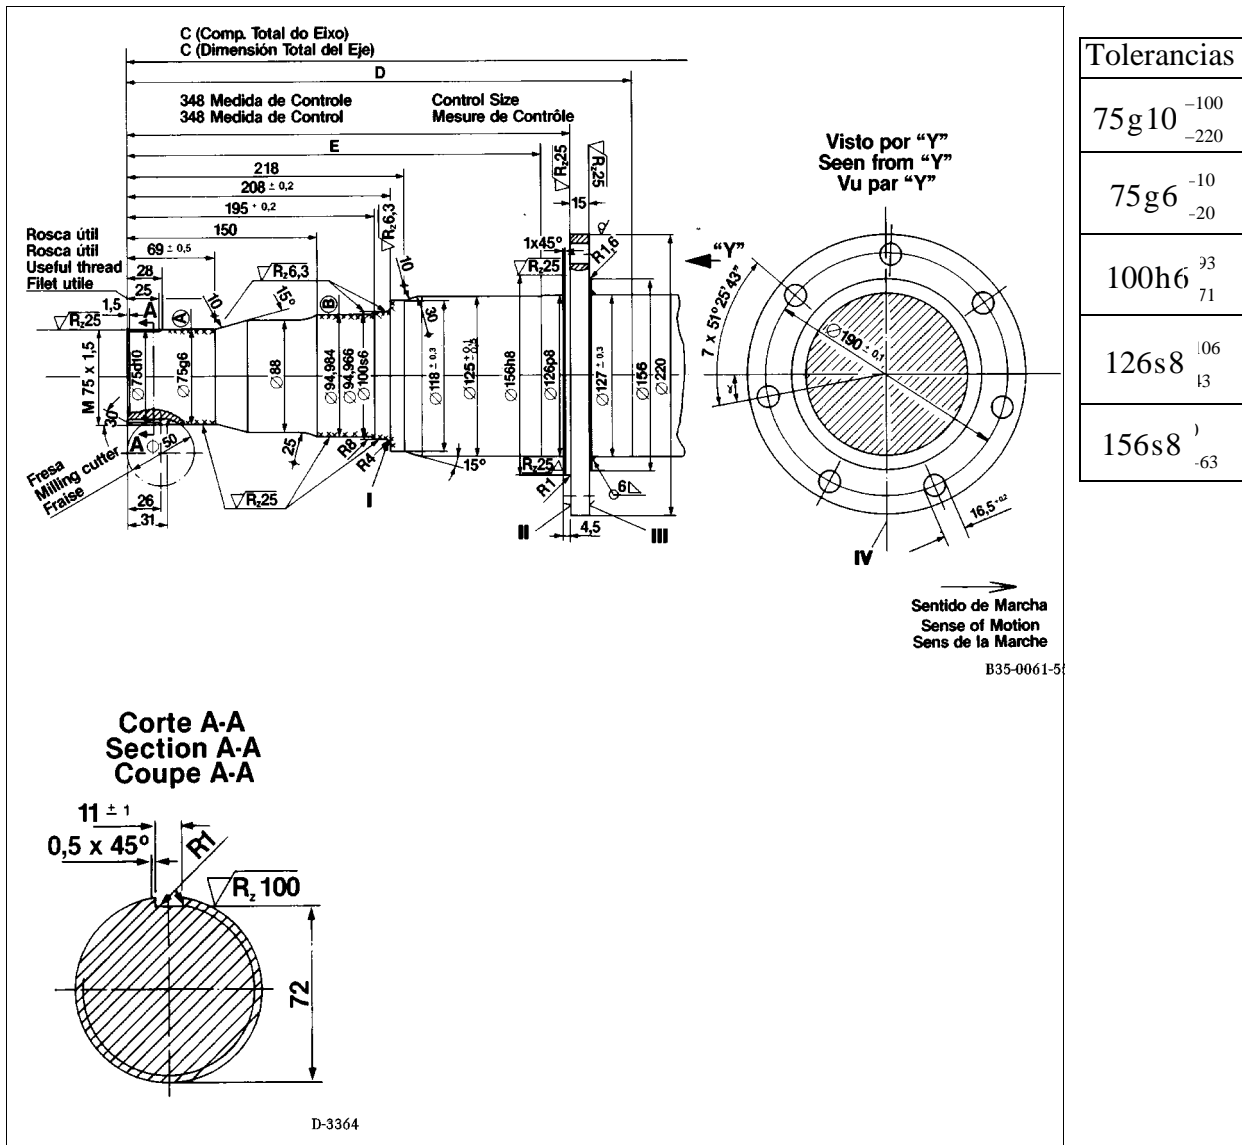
Maquinado de los extremos del eje (HL 4/26D - 9,2; HL 4/27D - 10; HL 5/2DZ - 10)
